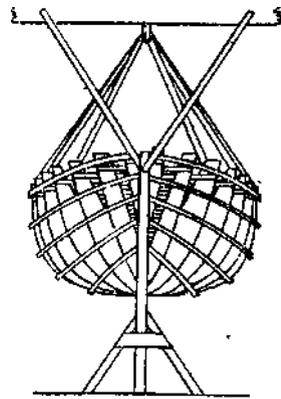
Вид на стапель с установленными лекалами и рыбинами.
